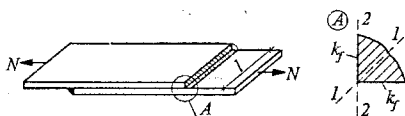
Кутовий зварний шов, який працює на зріз
